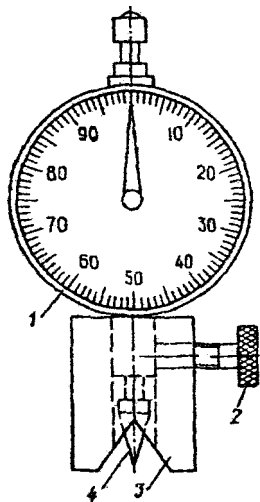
Приспособление для замера глубины повреждений: 1 – индикаторные часы; 2 – стопорный винт; 3 – основание; 3 – игла
